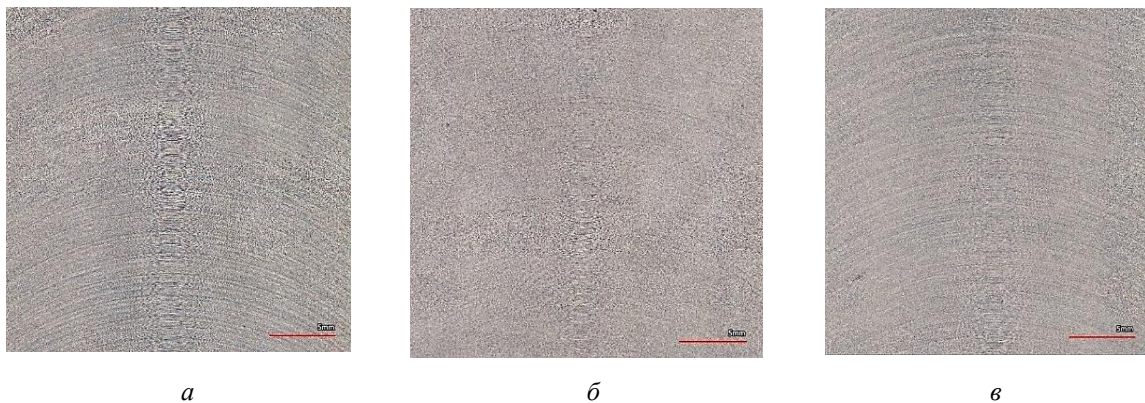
Скановані поверхні титанового сплаву після торцевого фрезерування:
